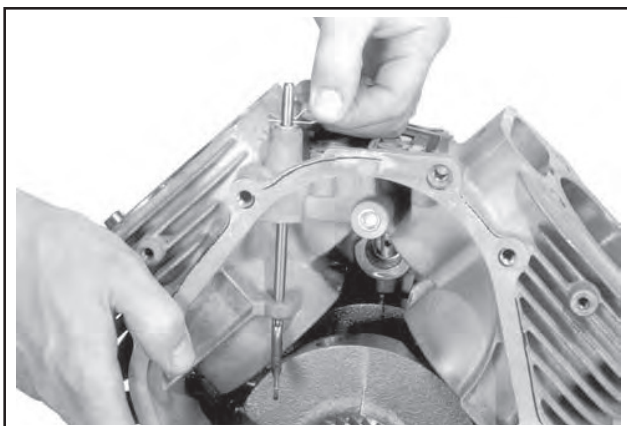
Entfernung des Befestigungsbolzens der Drehzahlreglerwelle (Größe Welle 6 mm).
